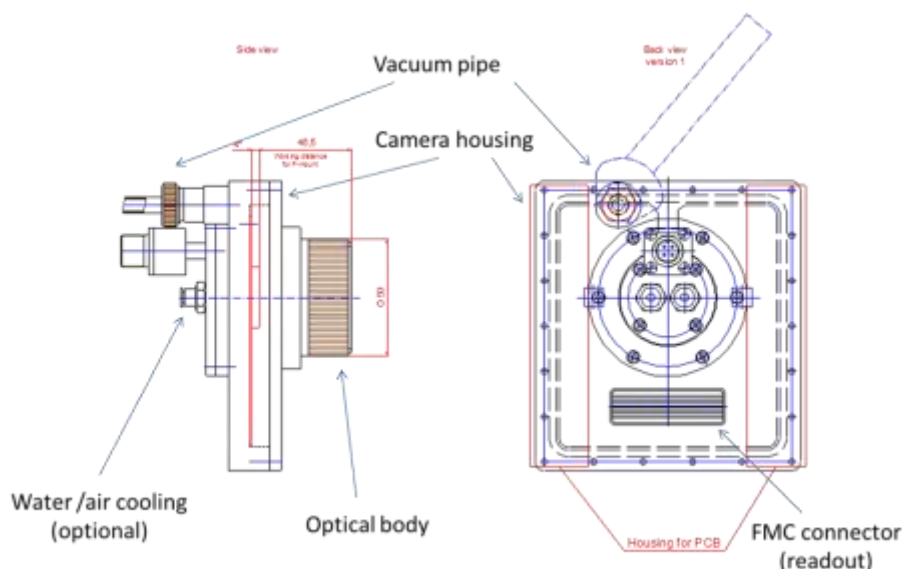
Чертёж корпуса для быстрой рентгеновской камеры. CMOS сенсор находится целиком внутри вакуумированного корпуса.
